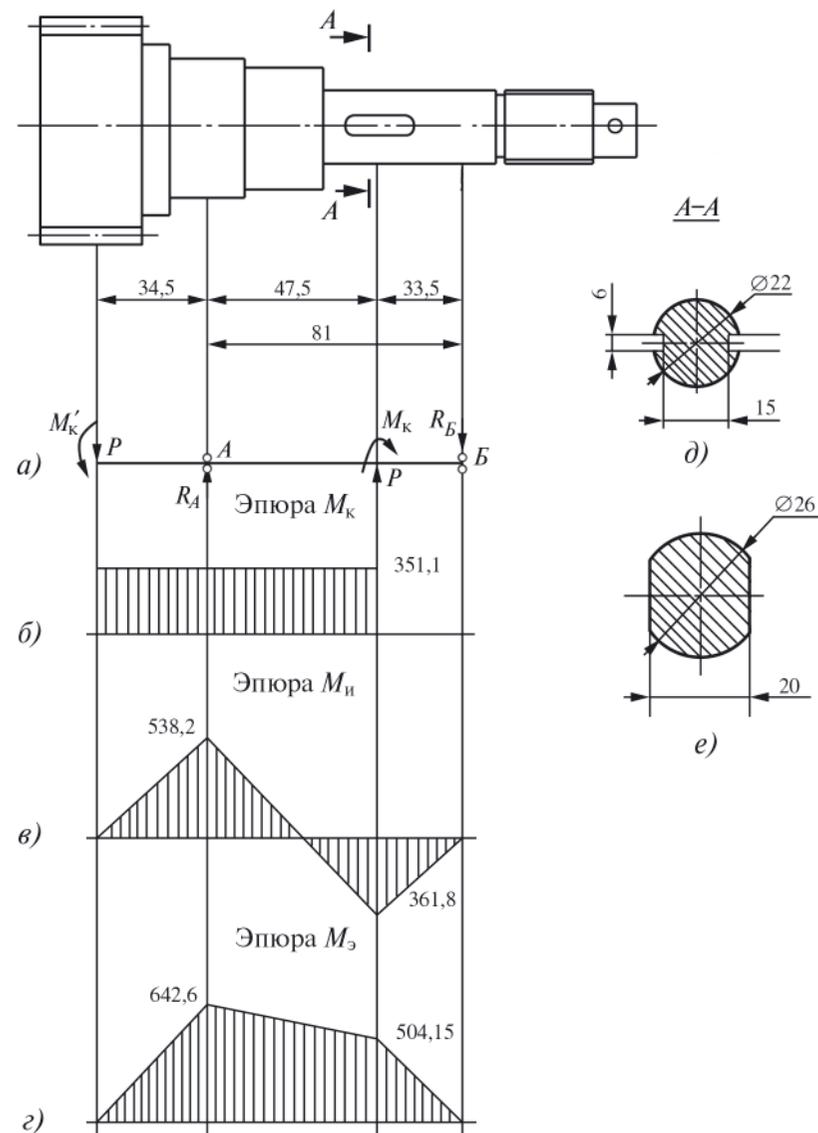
Эпюры моментов вал-шестерни выходного звена редуктора
